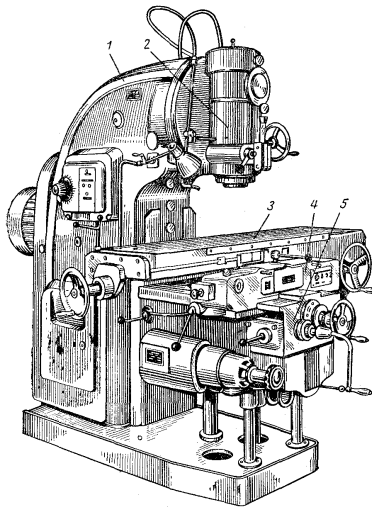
Вертикальний консольно-фрезерний верстат:
